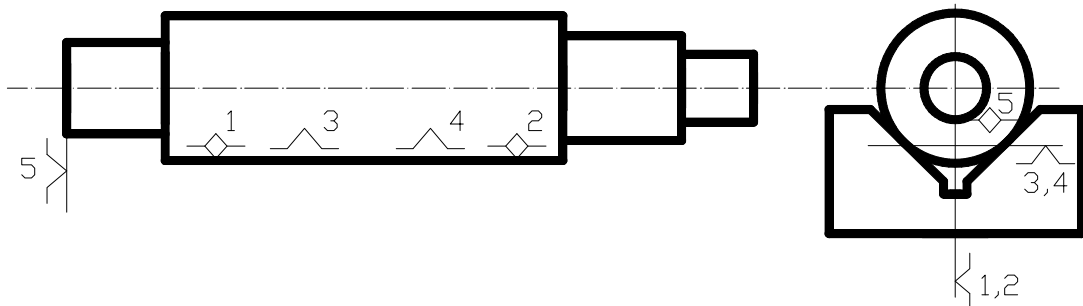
Чистові технологічні бази при свердлінні поперечних отворів та фрезеруванні шпонкових пазів (базування в призмах)
